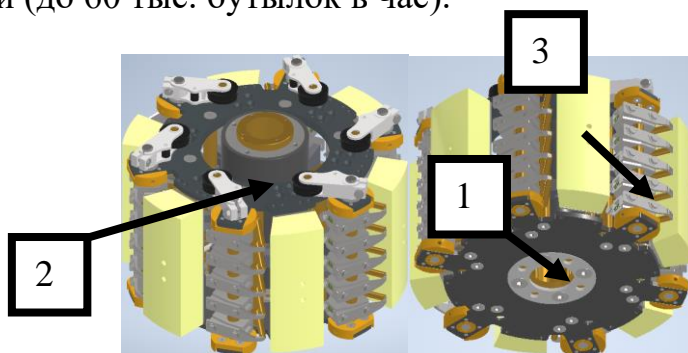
Общий вид сборочной единицы «Грейферный барабан»
